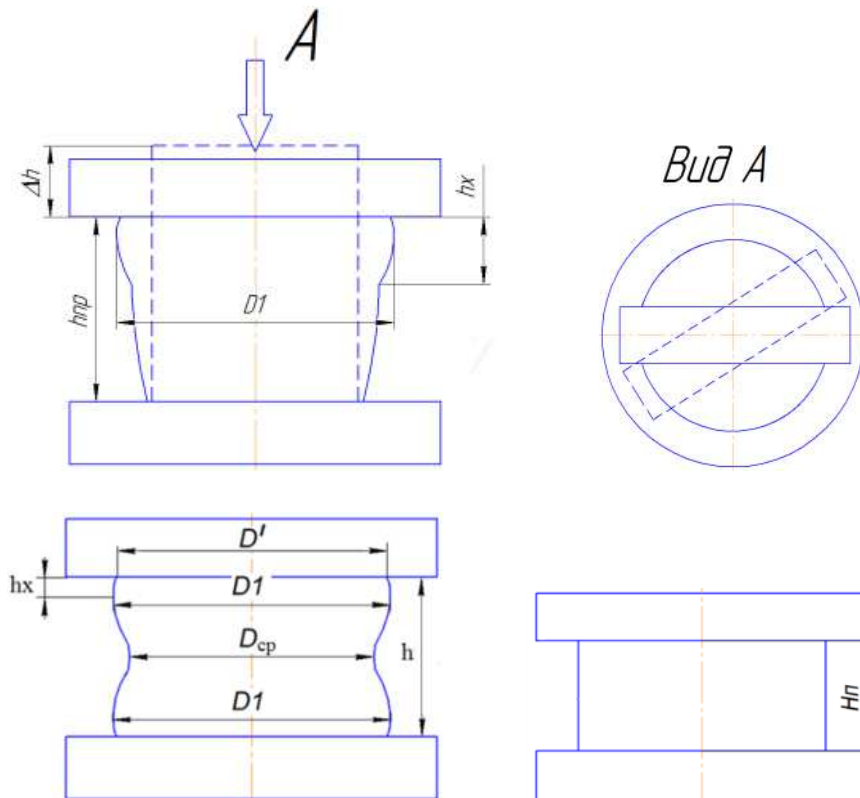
Схема осадження циліндричної заготовки з попереднім профілюванням розгонкою вузьким бойком
